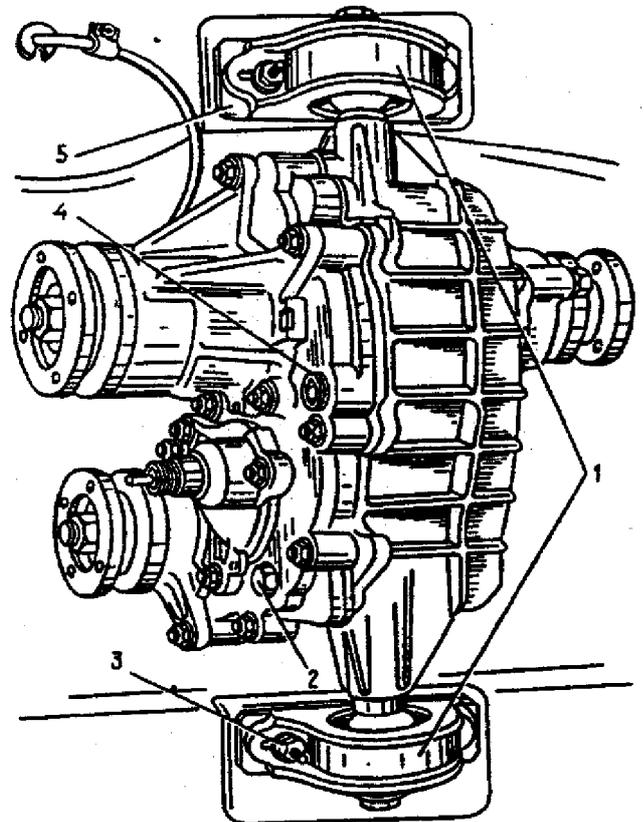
Fixação da caixa de transferência: 1 - suportes da caixa de transferência; 2 - bocal de abastecimento e verificação do nível de óleo; 3 - porca de fixação dos suportes; 4 - bocal de drenagem do óleo lubrificante; 5 - calços de regulagem.
